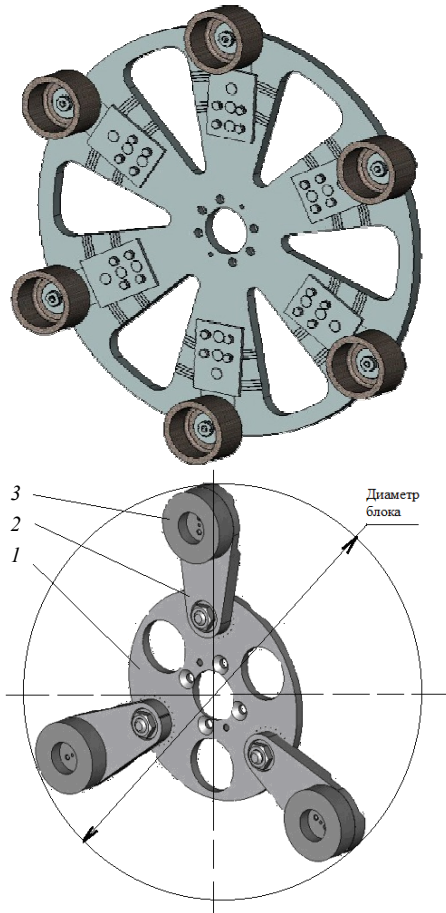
Конструкции инструментальных блоков на 6 и на 3 инструмента:
